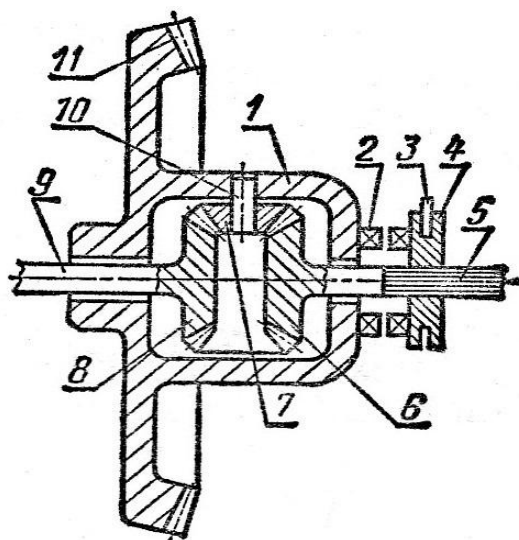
Схема дифференциала и механизма его блокировки: 1 – корпус; 2 – кулачок; 3 – вилка включения блокировки; 4 – подвижная муфта; 5,9 – полуоси; 6,8 – шестерни полуосей; 7 – сателлит; 10 – ось сателлита; 11 – ведомая шестерня главной передачи
